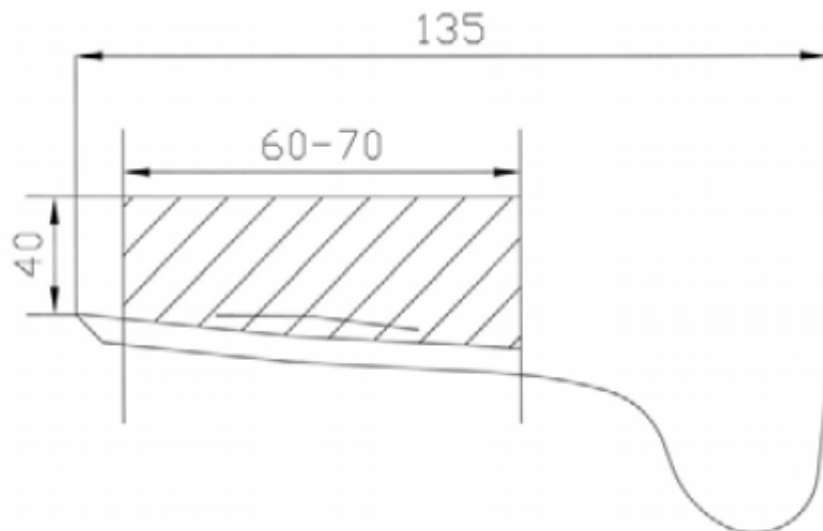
Zona de localización de fisuras circunferenciales en la llanta (medidas en mm).
